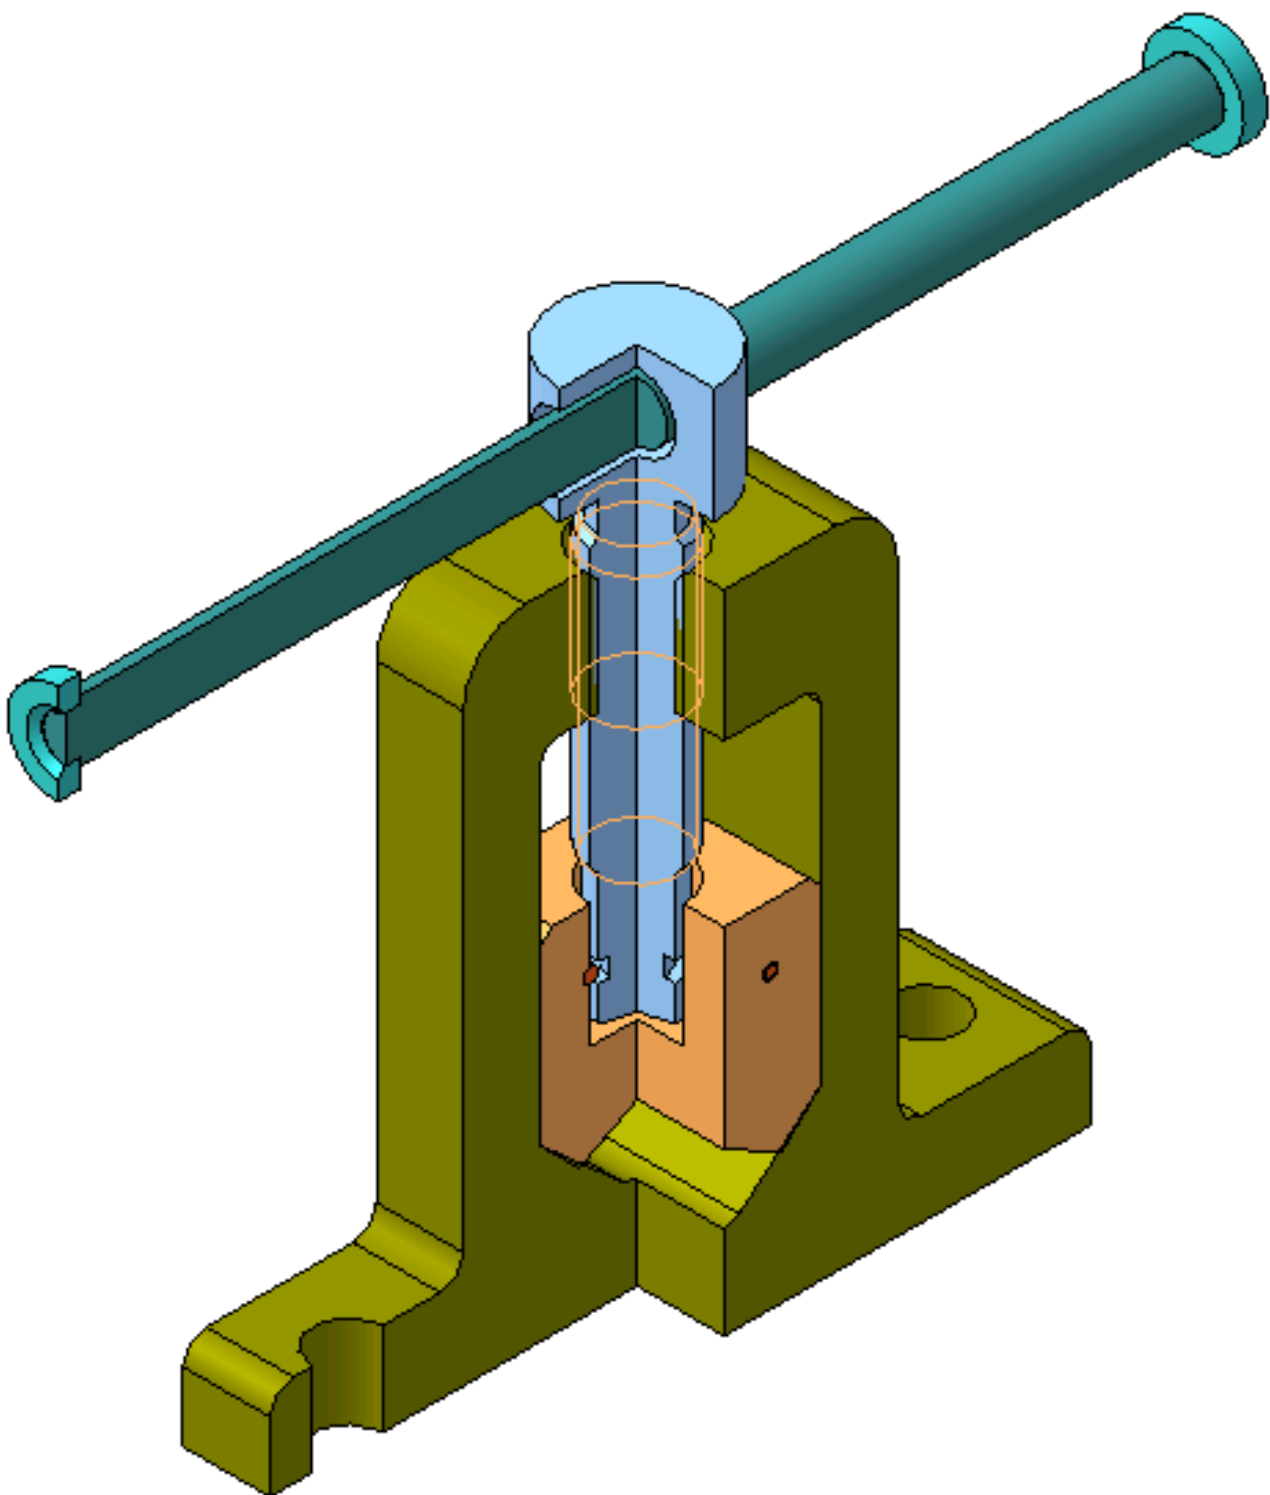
3D-модель сборки изделия «Тиски трубные» (варианты 16, 36)
